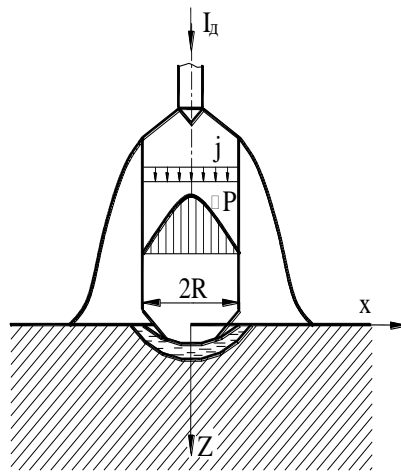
Цилиндрическая модель столба сварочной дуги
